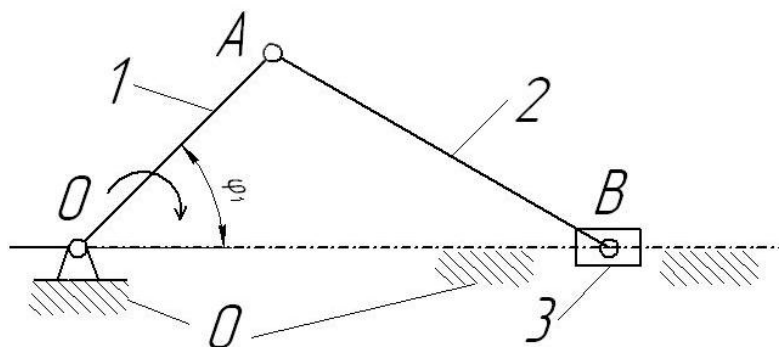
Кинематическая схема кривошипно-ползунного механизма
